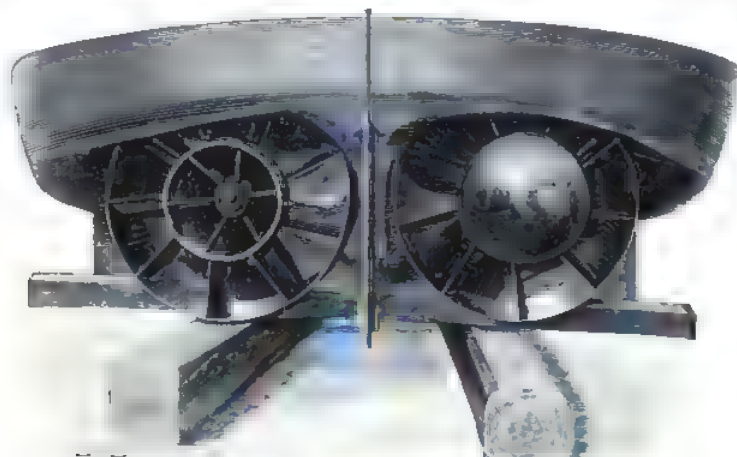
Ansicht der Schrauben-Turbinen-Propeller.
